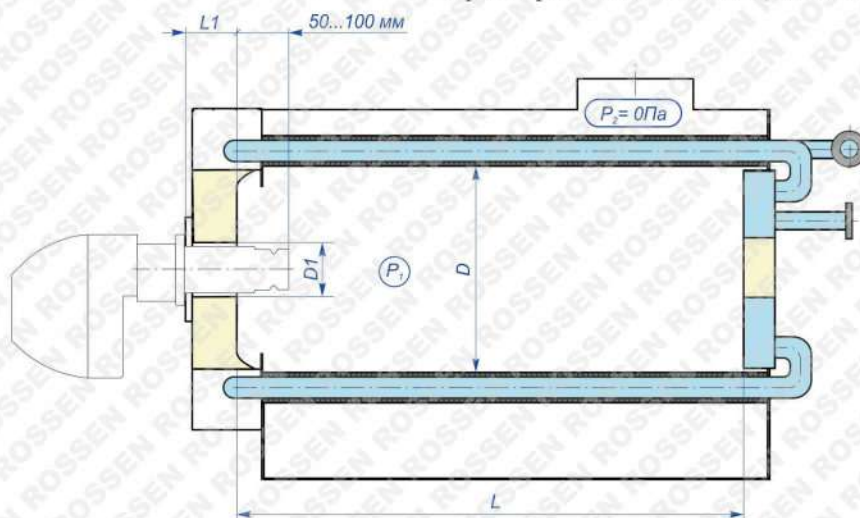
Габаритные и присоединительные размеры котлов RSD11000 – RSD17000
